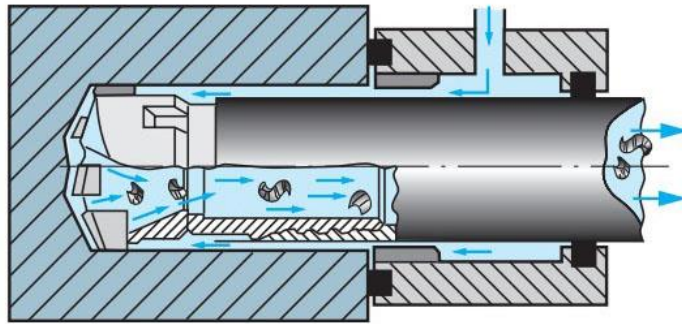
Схема одноштанговой системы STS (Single Tube System)
